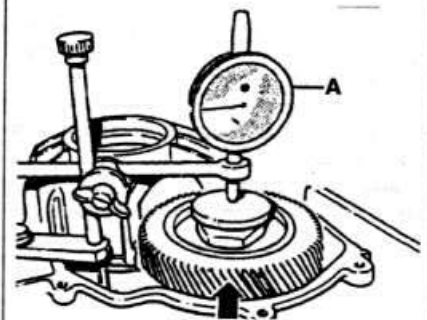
Измерение осевого перемещения ведущей вал-шестерни главной передачи:
